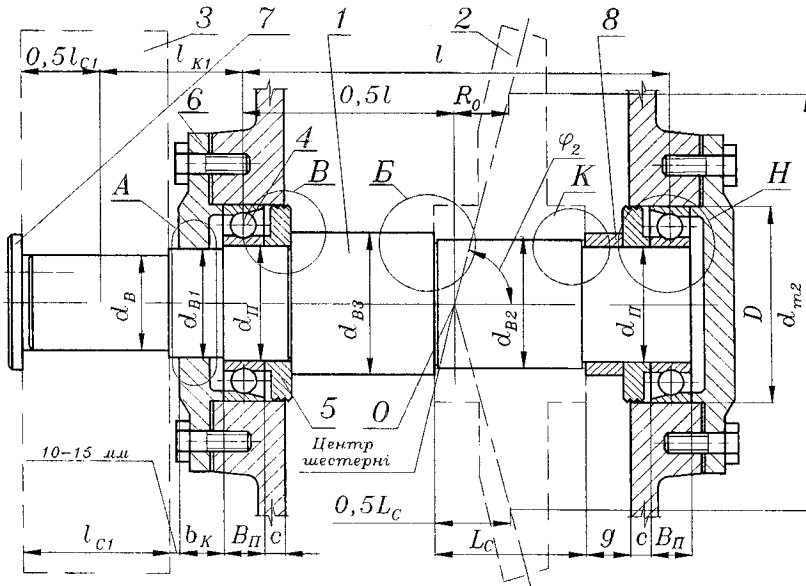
Ведений вал колеса закритої конічної зубчатої передачі
